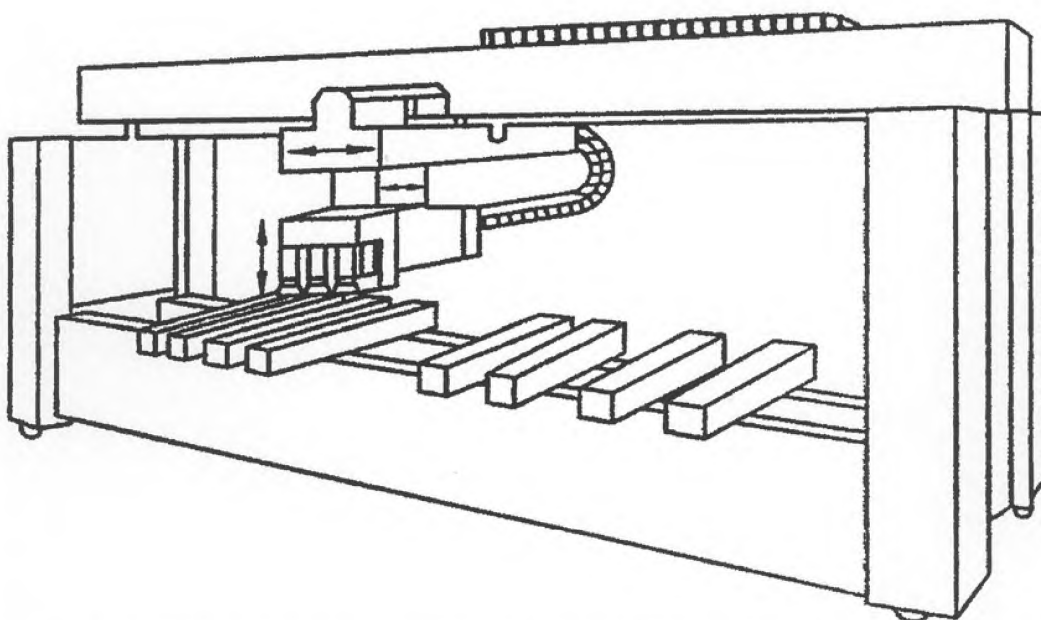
Станок портального типа (неподвижный портал, неподвижный стол, подвижная головка)¹
